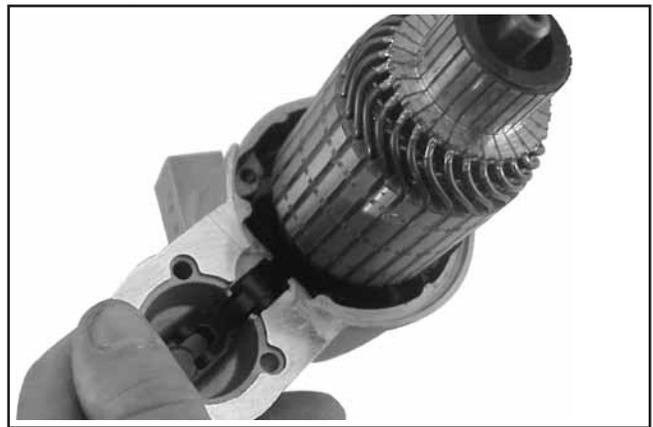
Instalar a Armadura e a Alavanca de Articulação.
